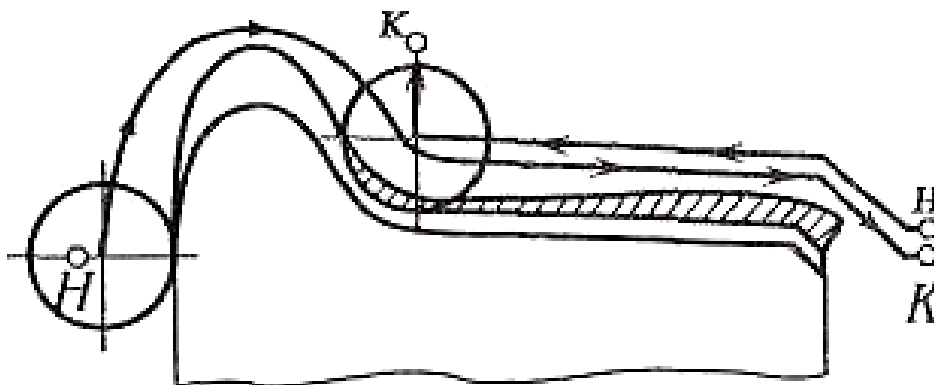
Схеми обробки профілю поверхні колеса на колесотокарному верстаті моделі 1836А
